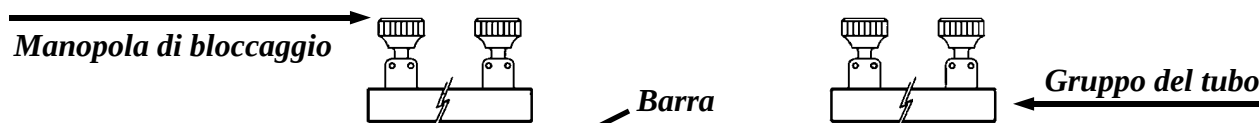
Posizione verticale ad angolo retto attraverso il raccordo trasversale
